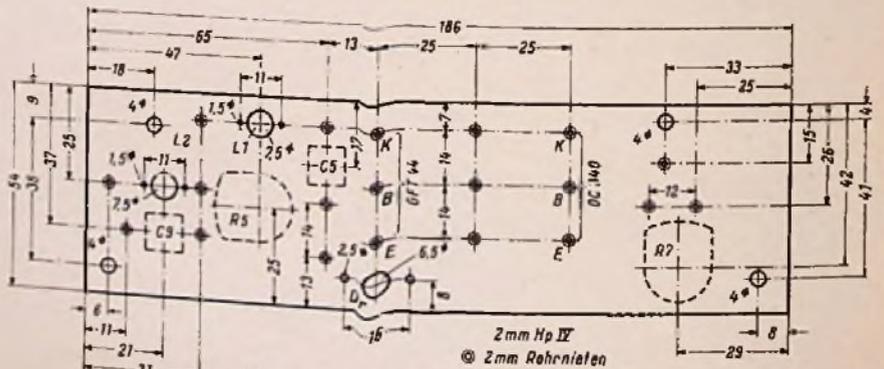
Die Maße der Montageplatte und die Anordnung der wichtigsten Teile
